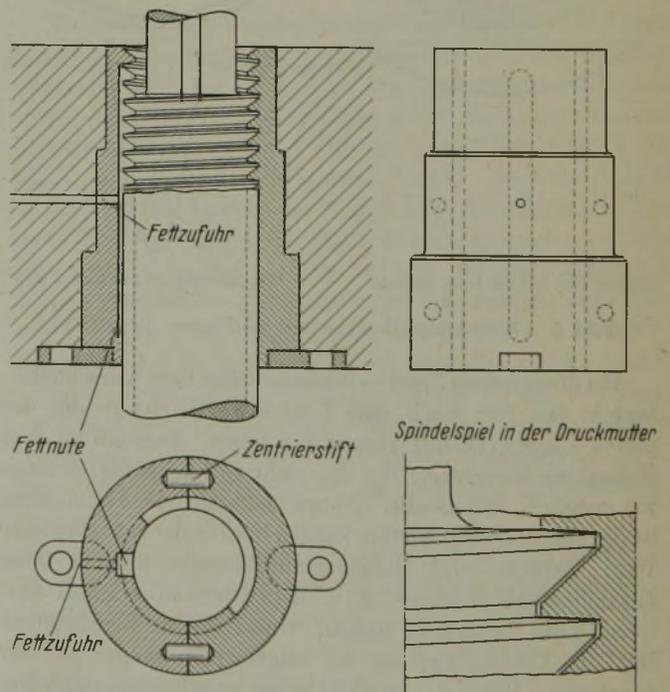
Druckmutter aus Stahlguß für Walzgerüst.
